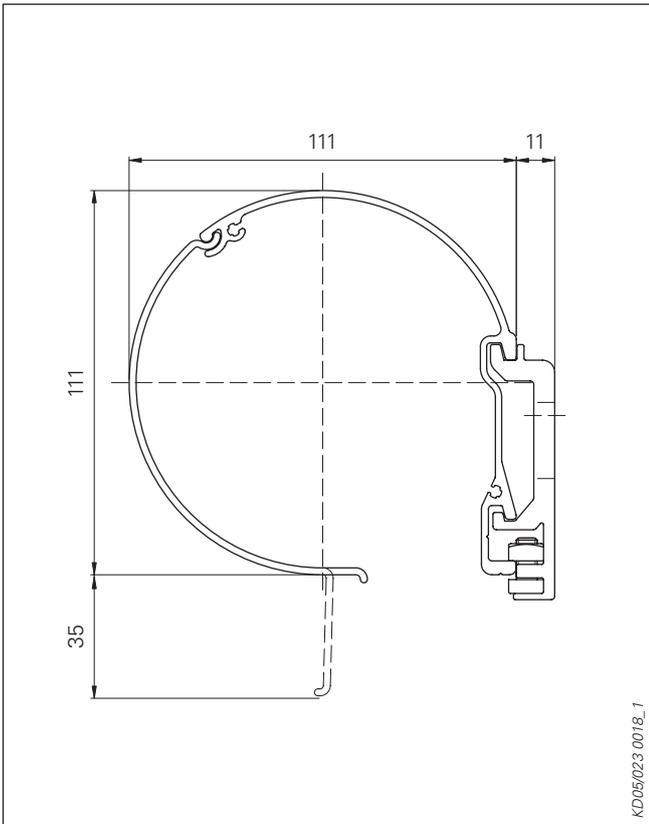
Montaje mural Modelo 46.3 y 47.3
